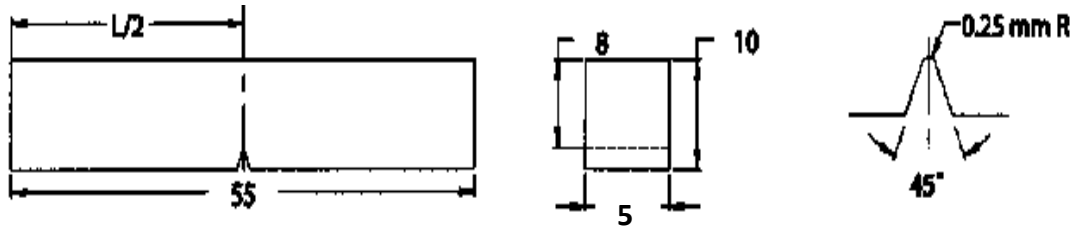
Dimensiones de probetas para ensayo Charpy.
